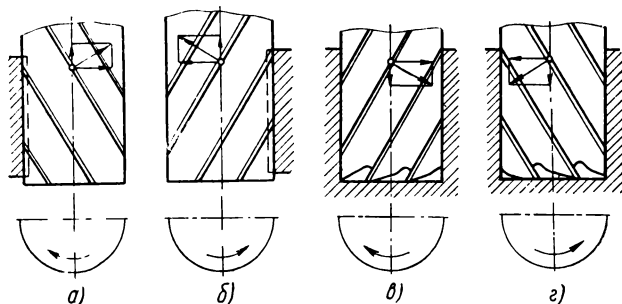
Направление винтовых канавок при фрезеровании концевыми фрезами:
